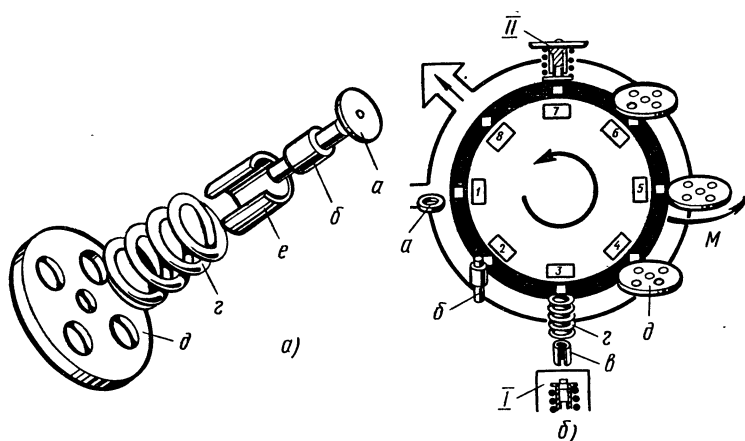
Клапан, состоящий из пяти деталей (а), схема его сборки (б)
